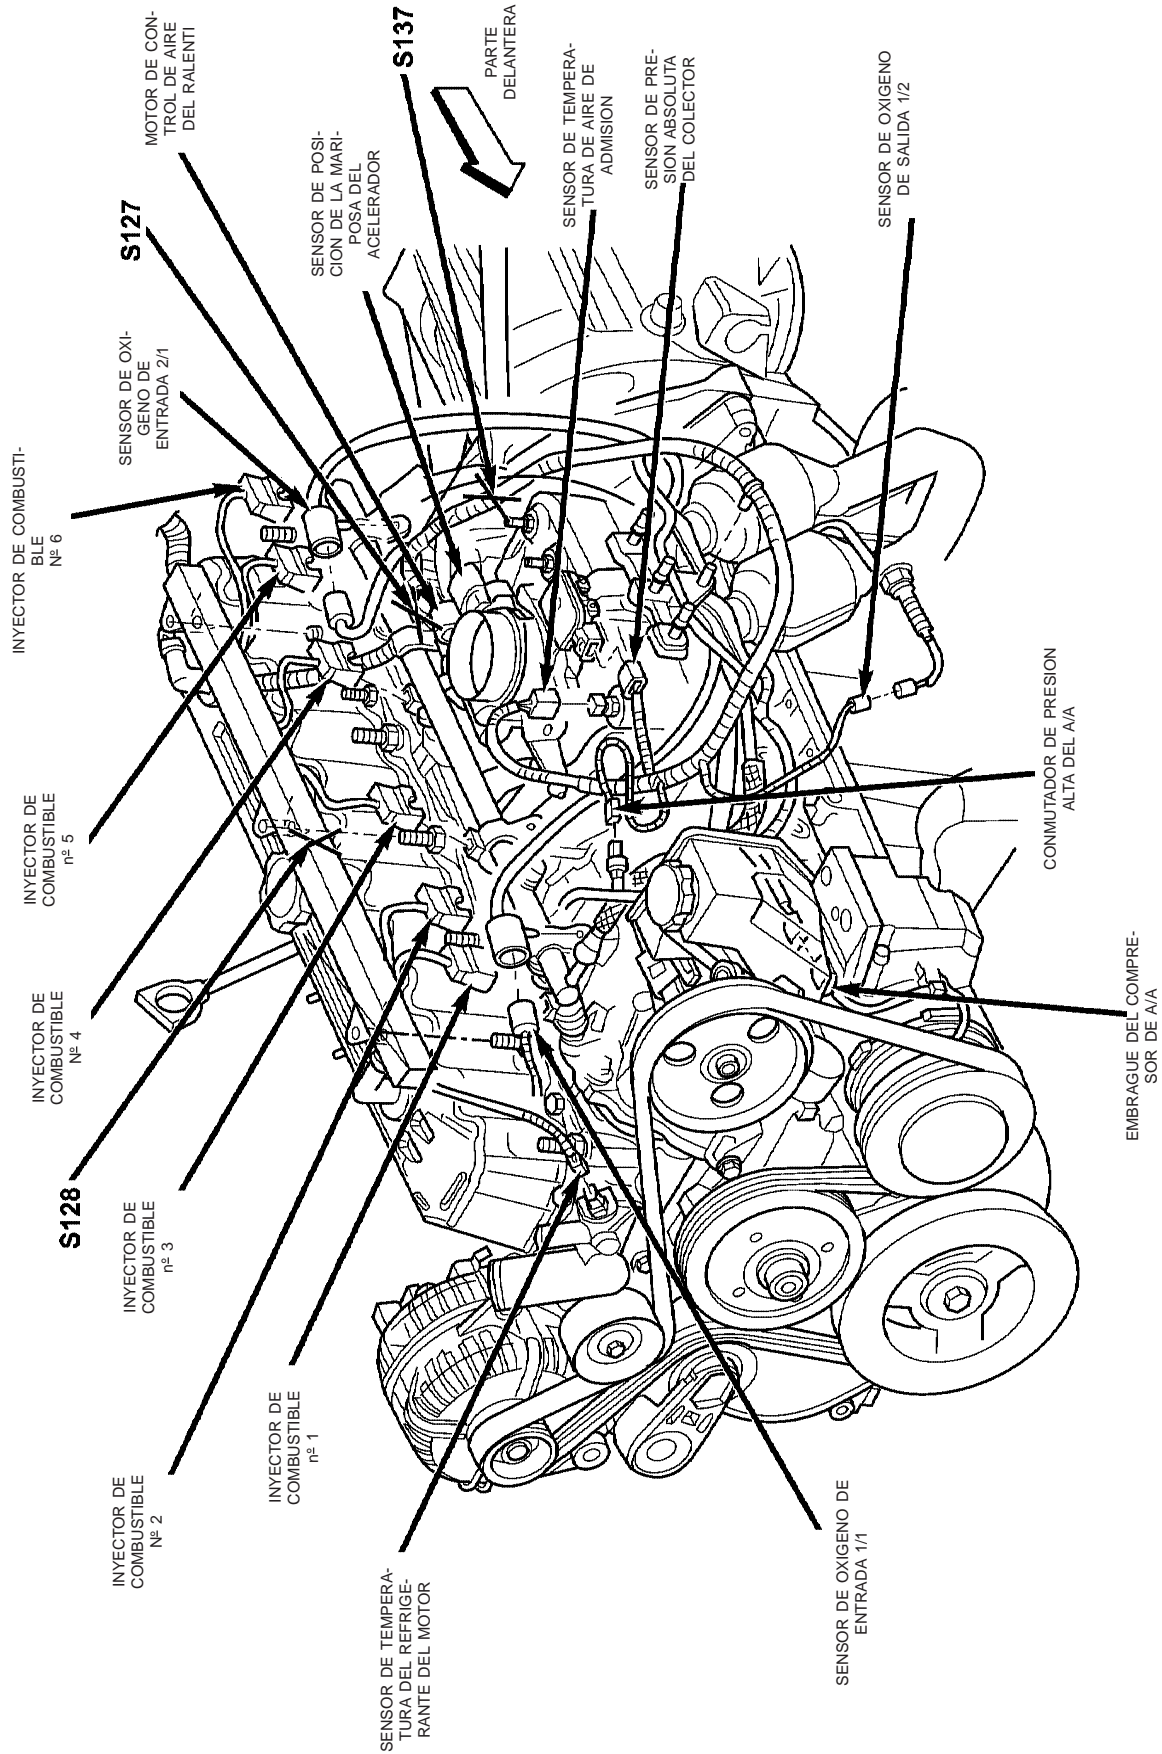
MOTOR 4.0L LADO IZQUIERDO
